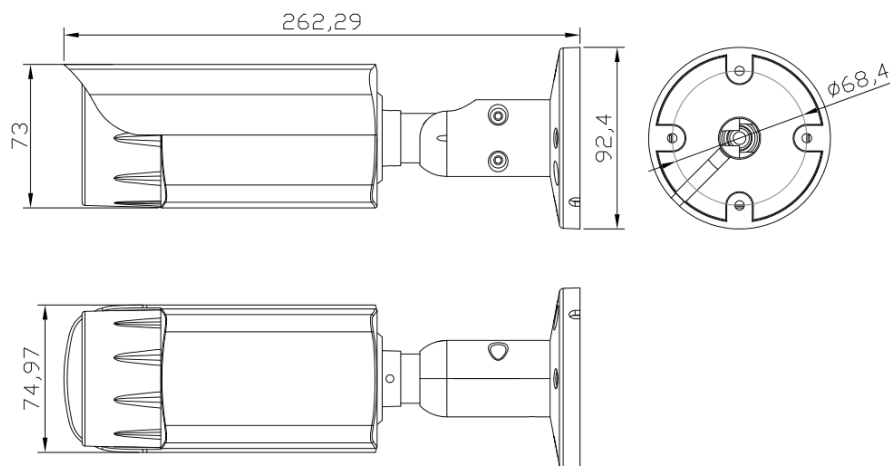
Габаритный чертеж видеокамеры ИВМ-501.
